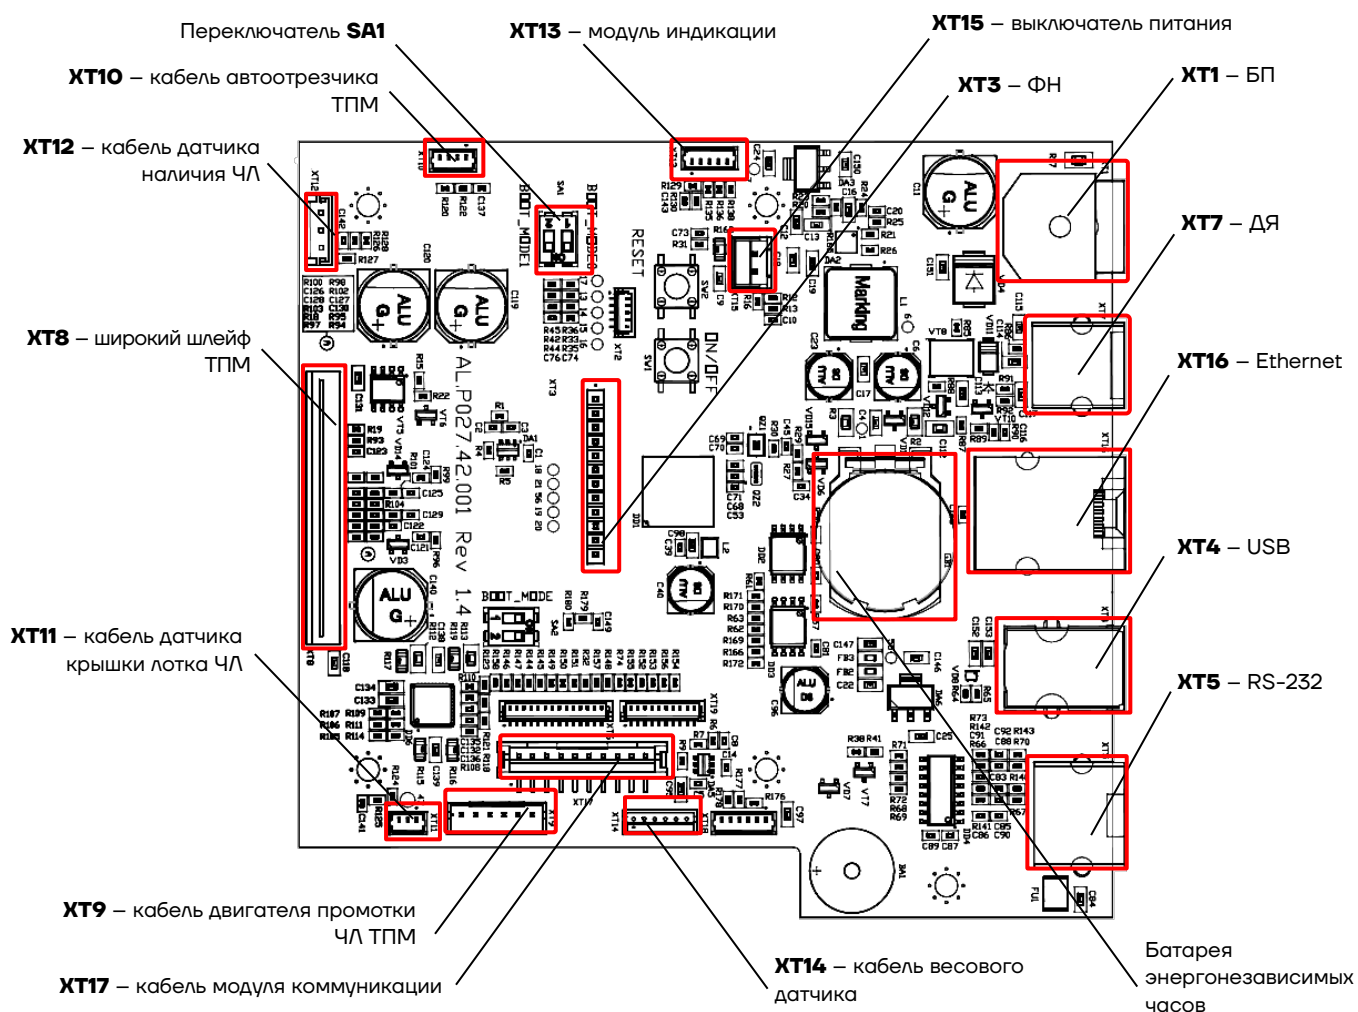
Расположение элементов блока управления AL.P027.42.000 (вид сверху)
